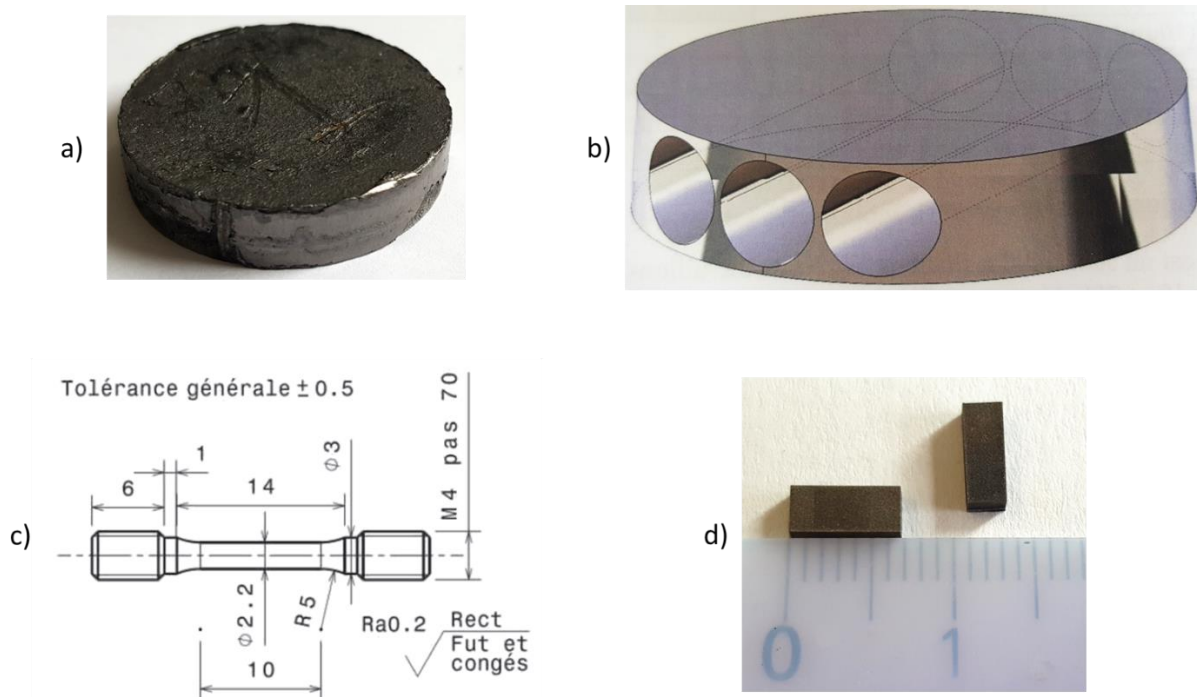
a) Pastille SPS Ø36h8mm, b) Carottage de trois cylindres pour l'usinage des éprouvettes de traction / fluage [142], c) Dimensions d'une éprouvette de traction / fluage [142], d) Éprouvettes de compression
